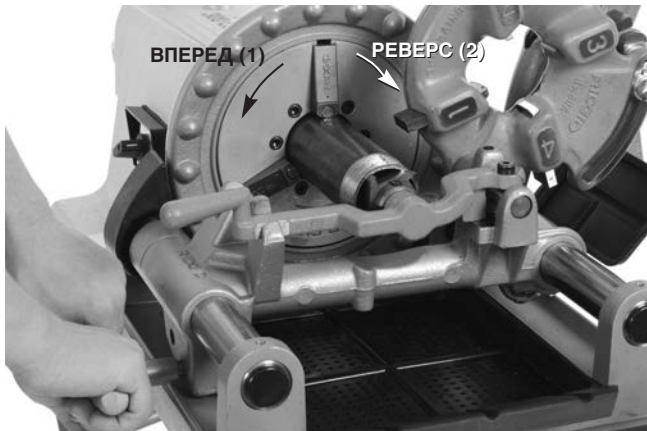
Зенкование трубы с помощью зенковки, вращение станка
